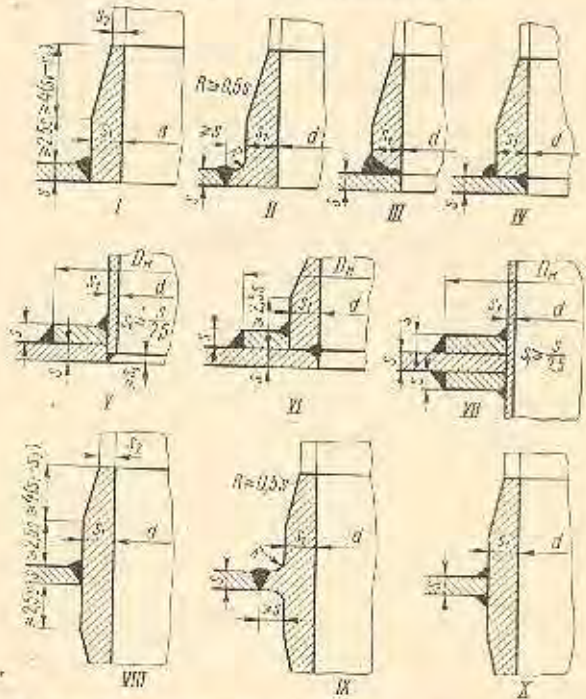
Основные типовые конструкции укрепления отверстий для приварных штуцеров и труб в сварной аппаратуре (из пластичных материалов), работающей при статических нагрузках. Укрепление присоединяемых труб: I—IV — втулочное; V — накладочное; VI — втулочное-накладочное. Укрепление ввода труб: VII — накладочное; VIII—X — втулочное
